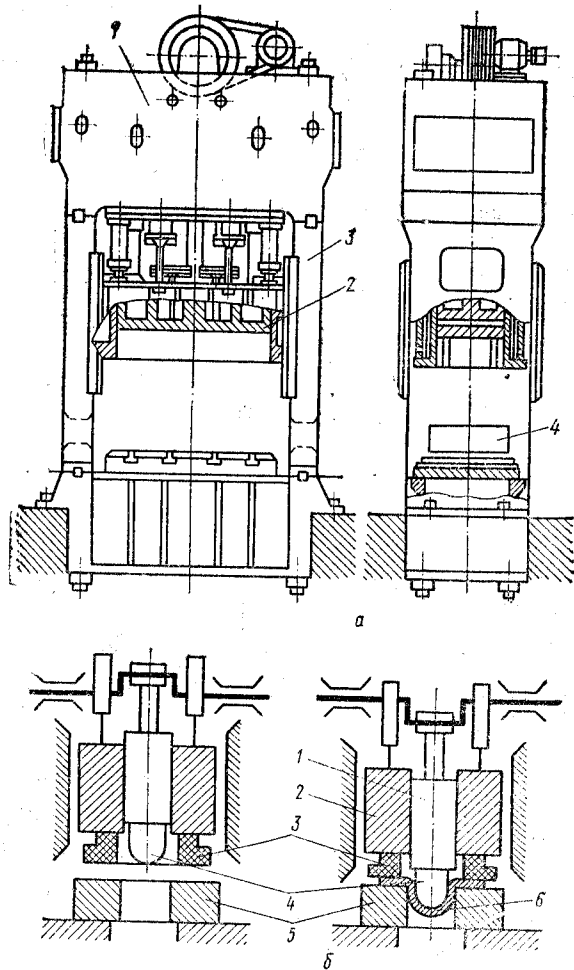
Общий вид кривошипного пресса (а) и схема работы пресса двойного действия (б)
